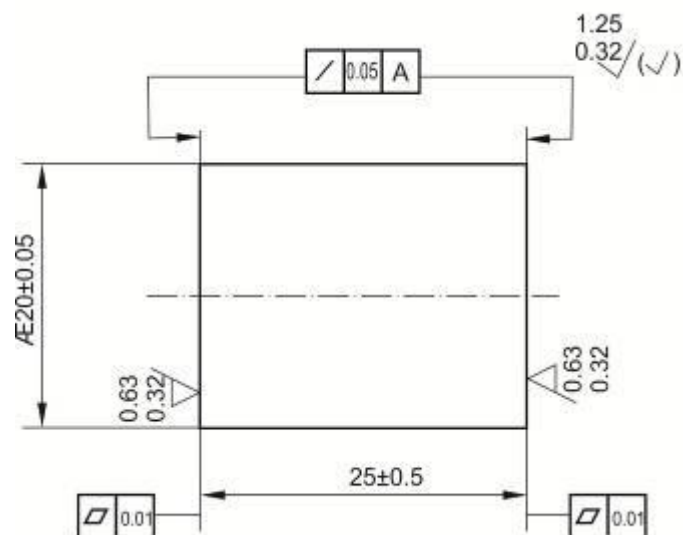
Образец для испытаний на изнашивание при фреттинг-коррозии.
